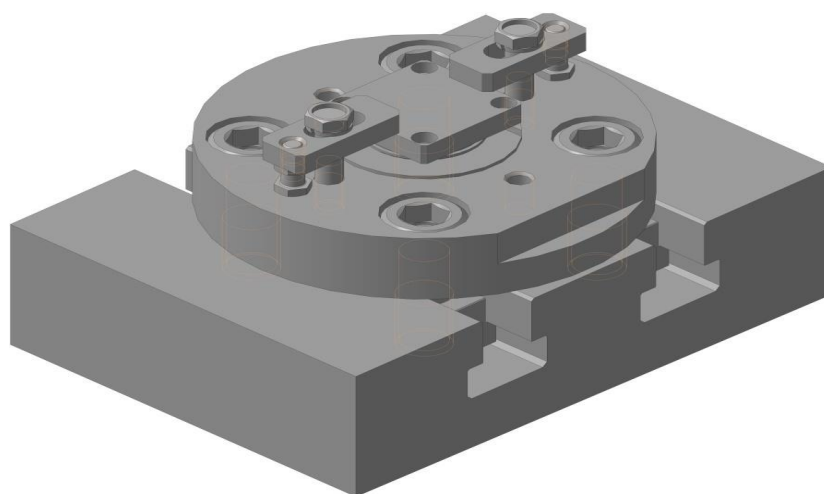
Специальное приспособление для операции фрезерная с ЧПУ
